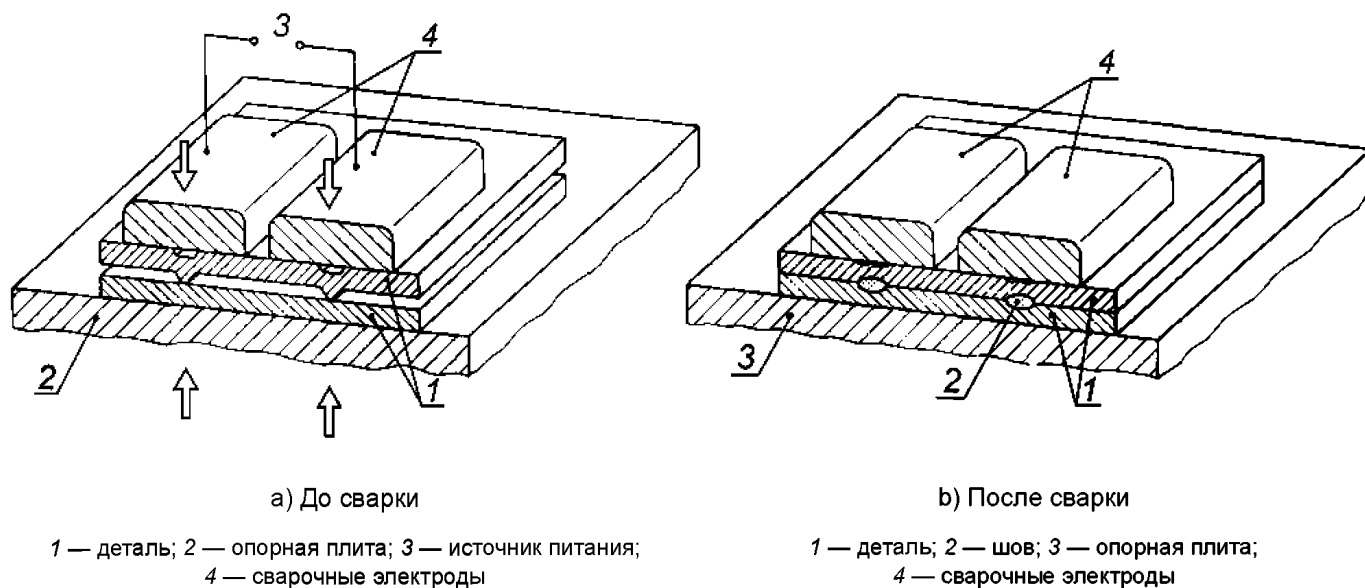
Сварка контактная рельефная односторонняя
